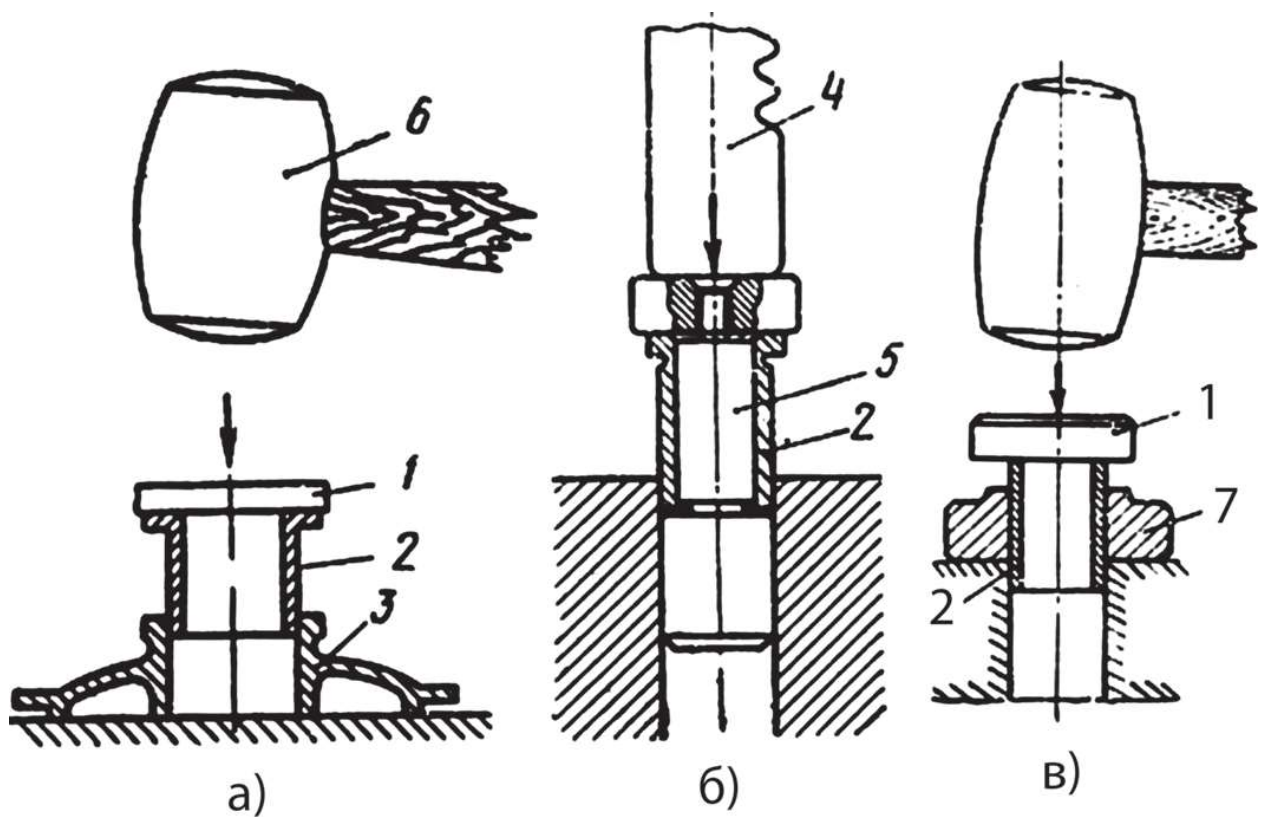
Запрессовка втулок в корпус подшипника: а — с помощью накладки; б — с помощью ручного пресса; в — с направляющим кольцом; 1 — накладка; 2 — втулка; 3 — корпус; 4 — шток пресса; 5 — оправка; 6 — молоток; 7 — направляющее кольцо
